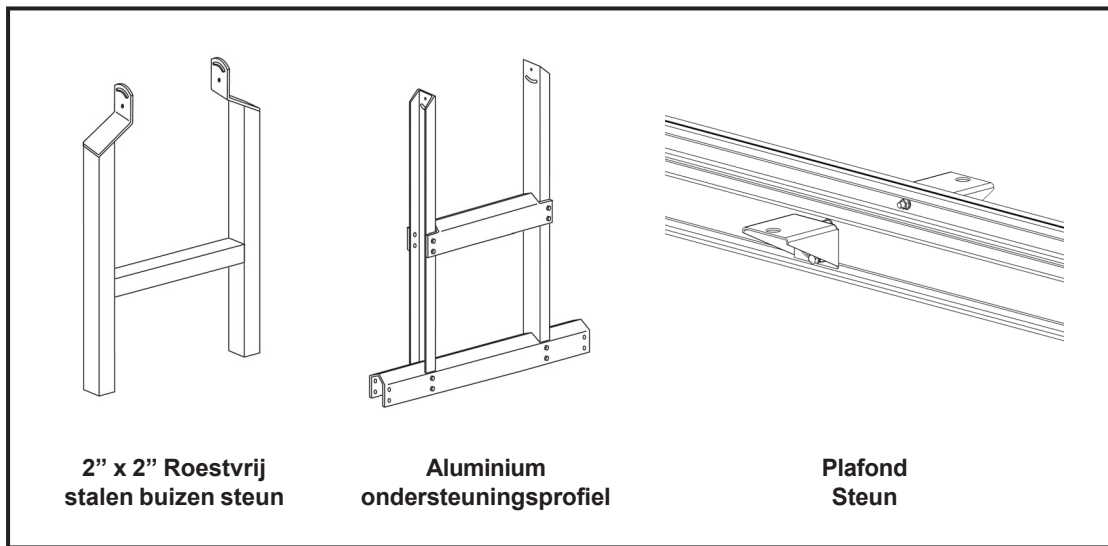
Overzicht van het centrale steunrails-systeem voor retourketting
